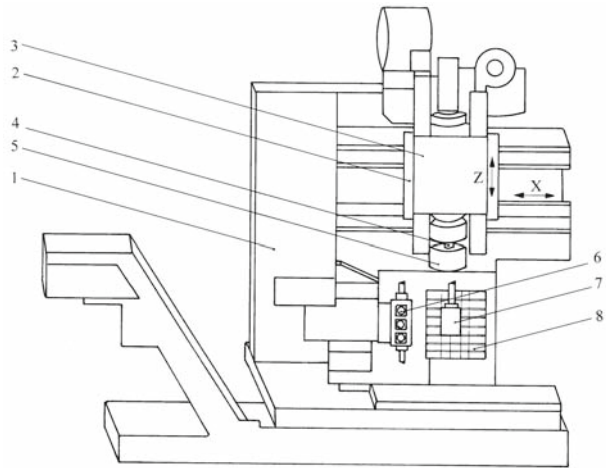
Grundaufbau der Senkrechtdrehmaschine mit Linearantrieben ohne Verkleidung (Deckel Maho Gildemeister)
